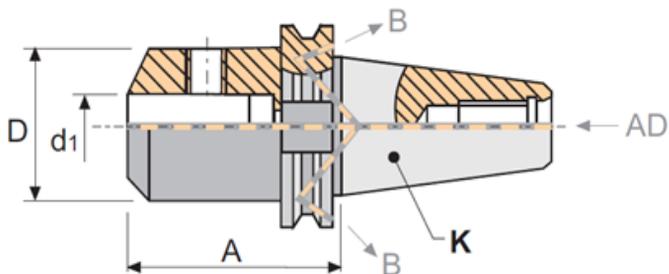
Патрон Weldon SK40-SL32-100 по DIN69871
